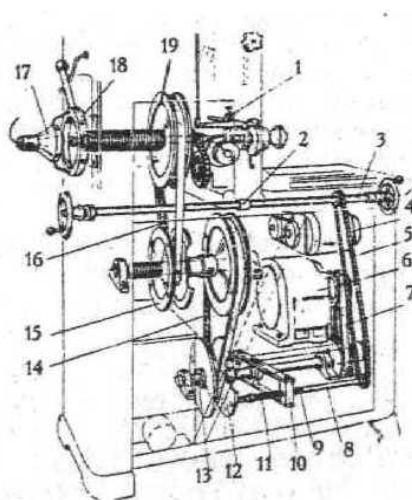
Схема подачи топлива в мензурку. Рис.4. Кинематическая схема стенда «Хартридж»: 1 — рычажный механизм; 2 — муфта; 4 — электродвигатель подкачивающего насоса; 12 — звездочка; 14, 16 — клиноремённые передачи; 17 — лампа неоновая; 18 — подшипник; 19 — шкив.
